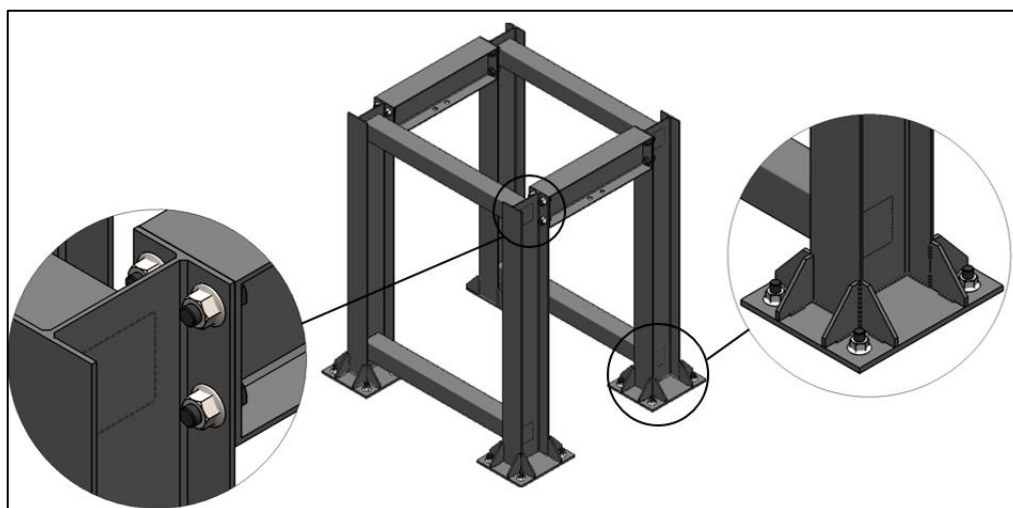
Representação esquemática da estrutura metálica de viga destacando os componentes de fixação
